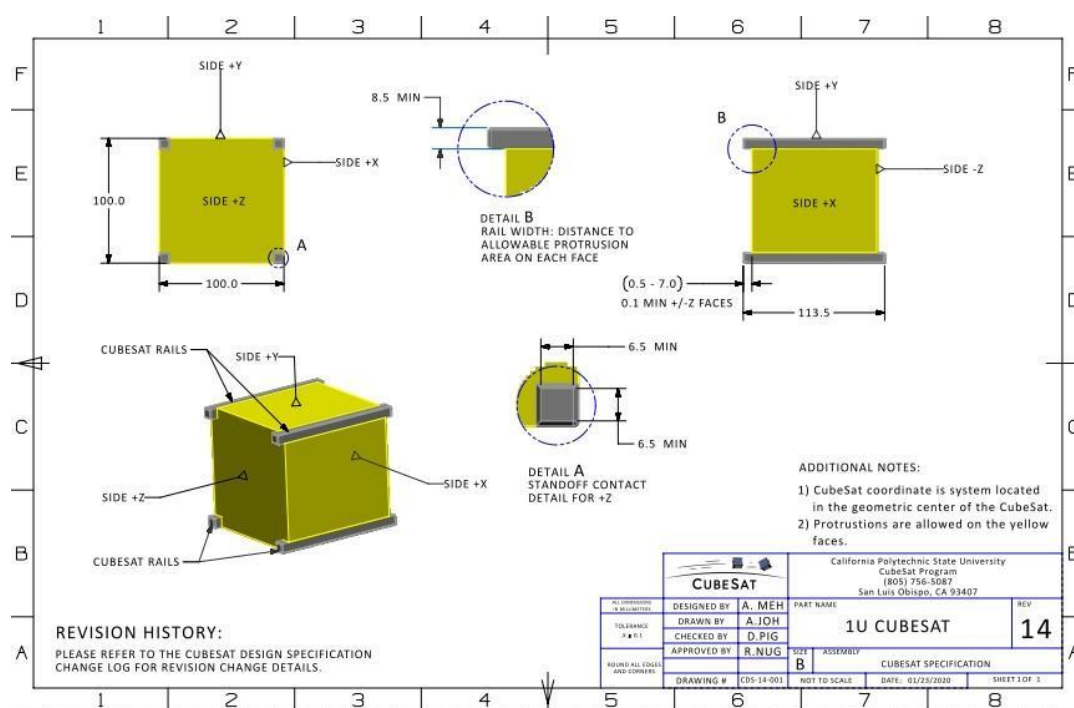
Чертеж спутника формфактора кубсат 1u
